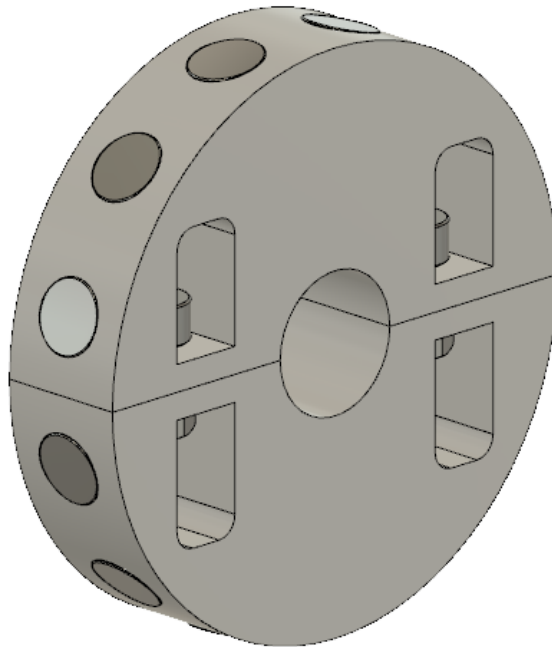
Ensamblaje de la pieza montada en el eje trasero del robot
